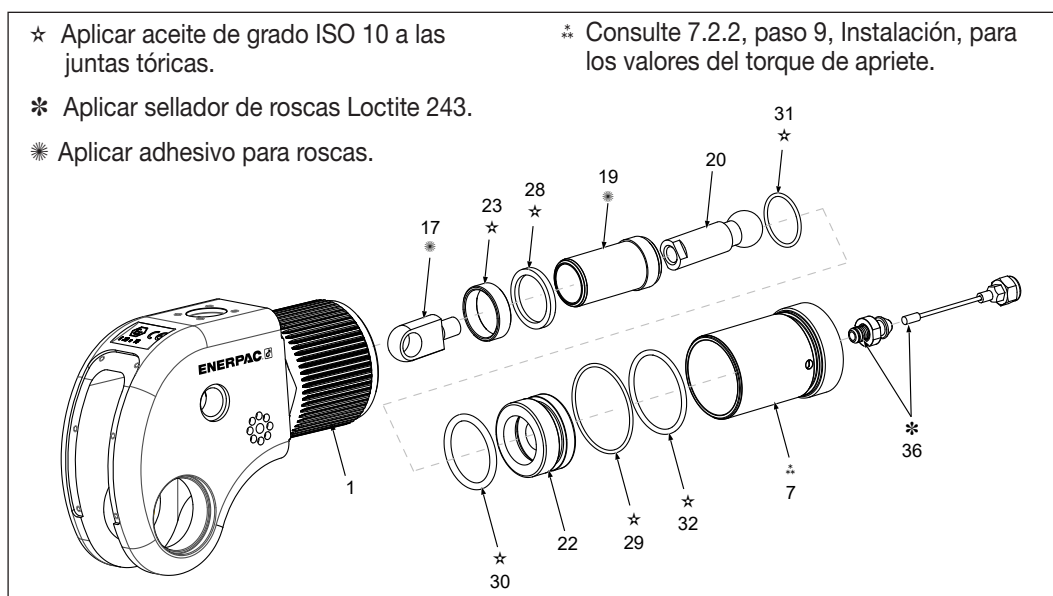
Pistones DSX1500, DSX3000, DSX5000 en despiece
